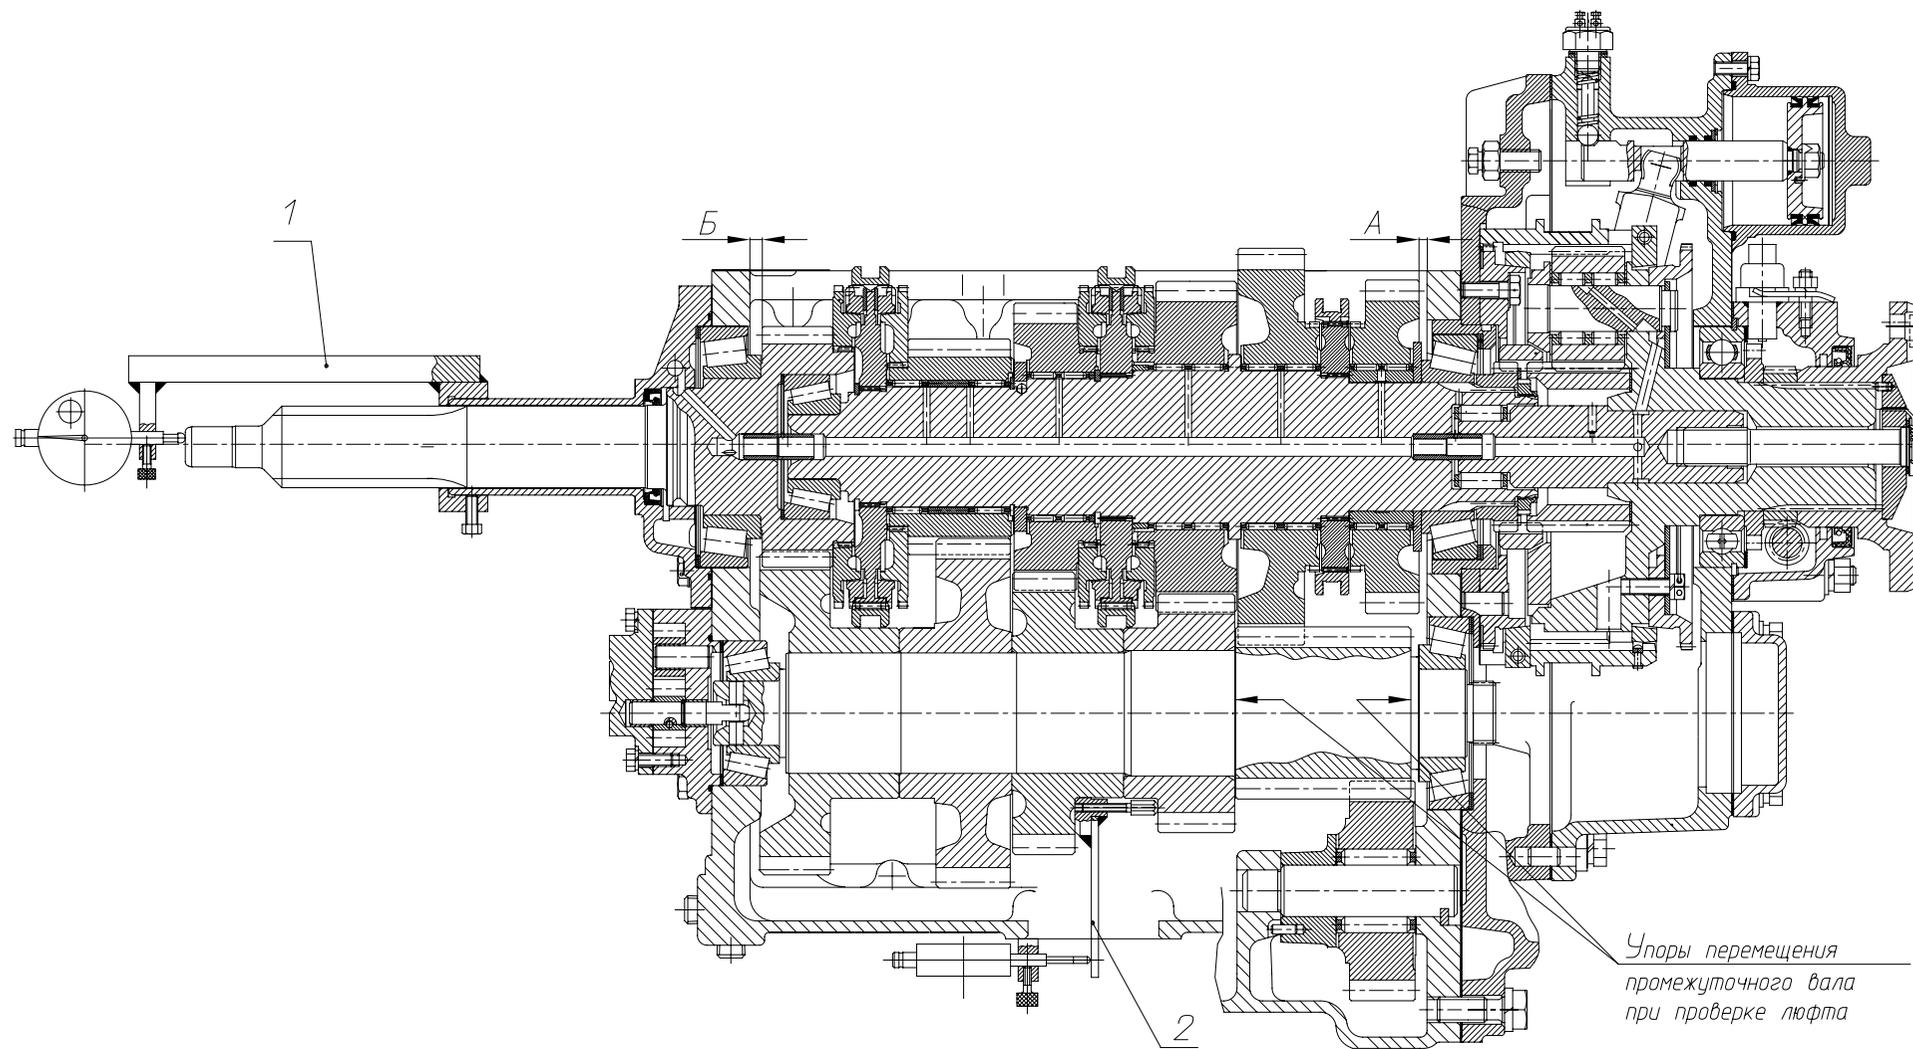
Приспособление для замера осевого люфта промежуточного вала:
